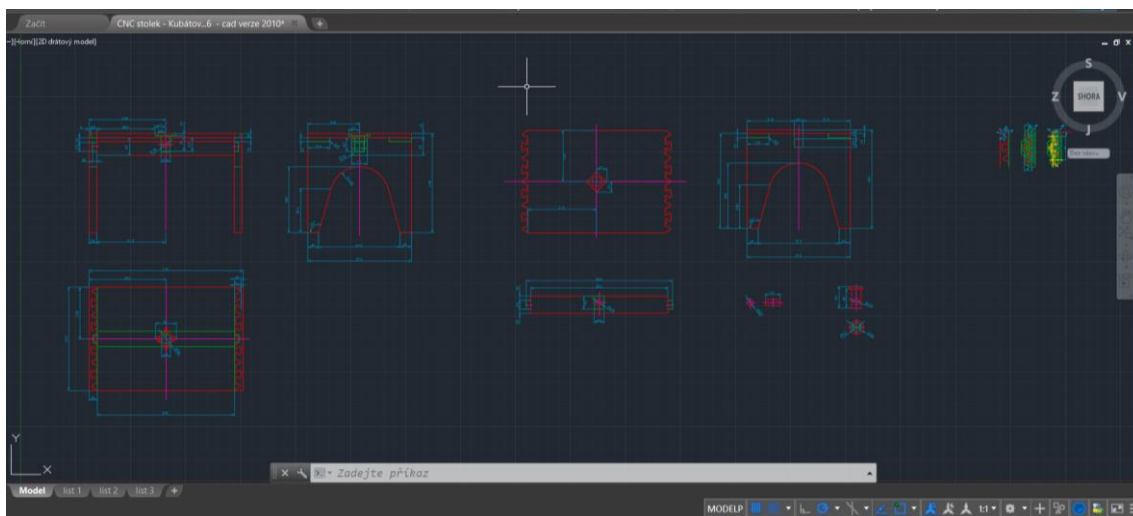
Nárys, bokorys a půdorys stolku se základními rozměry.
